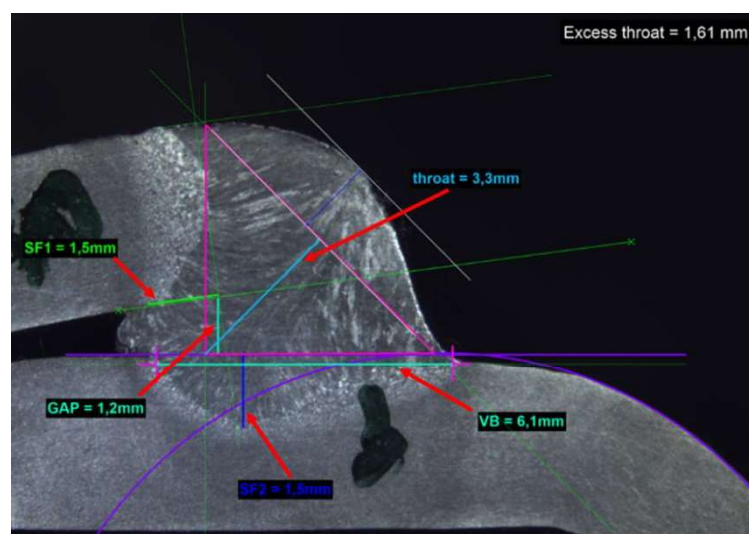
4 - Macrografia de uma soldadura (cortesia da MCG).
